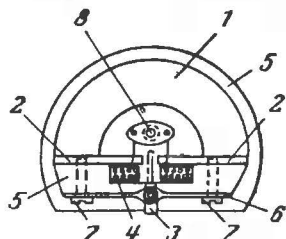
Электромагнитный звукосниматель ЭМЗ-Г завода «Молот». 1—постоянный магнит; 2—полюсные наконечники; 3—якорь; 4—катушка; 5—пластмассовый корпус; 6—стальная плоская пружина; 7—латунные винты; 8—отверстие с резьбой М5 для закрепления рекордера.
